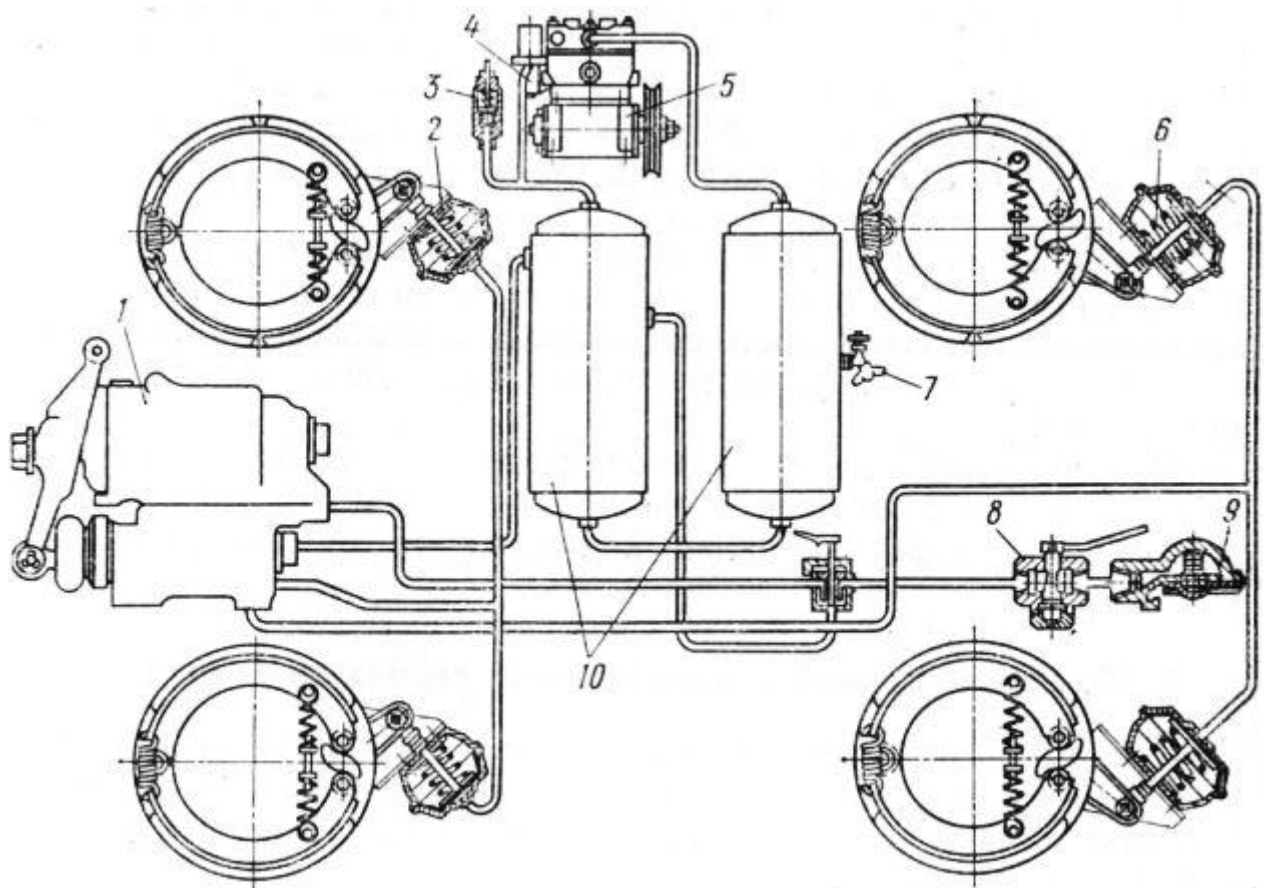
Схема пневматического привода тормозной системы автомобиля МАЗ-500А:
